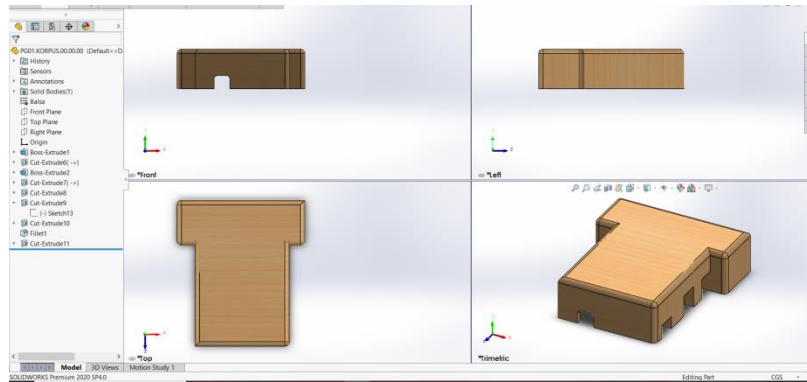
Сконструйований корпус в середовищі SOLIDWORKS
